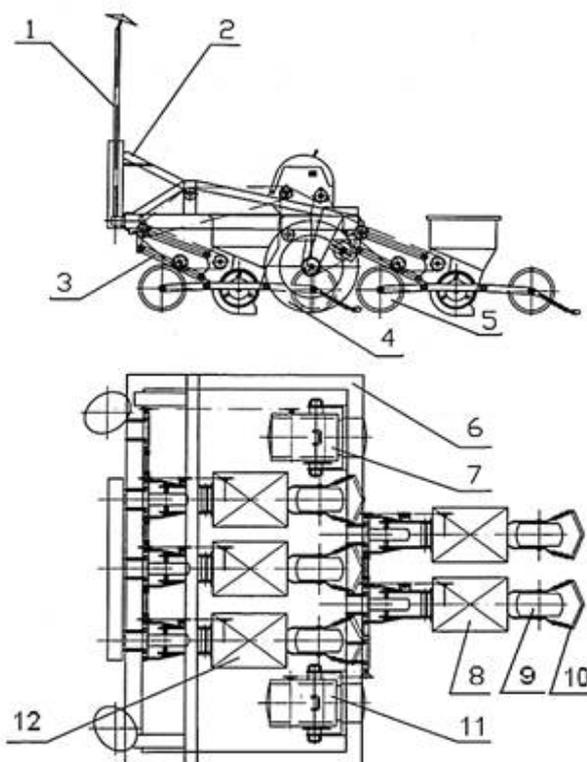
Схема расположения маркера 1 - маркер; 2 - навесное устройство; 3 - механизм параллелограмный; 4 - колесо опорно-приводное; 5 - колесо опорное
